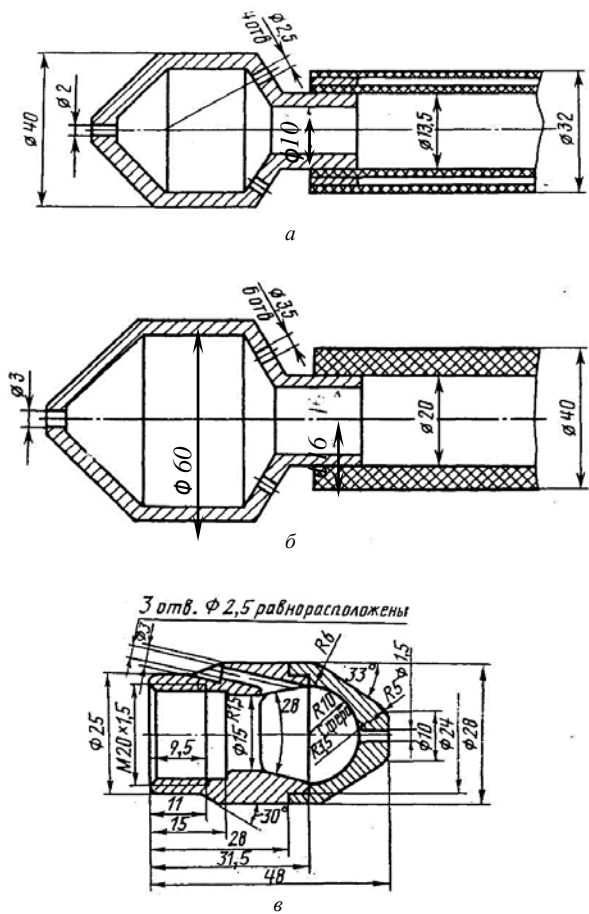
Конструктивные размеры головок: а – с двухслойным шлангом; б – для промывания коллекторов; в – для промывания дрен
